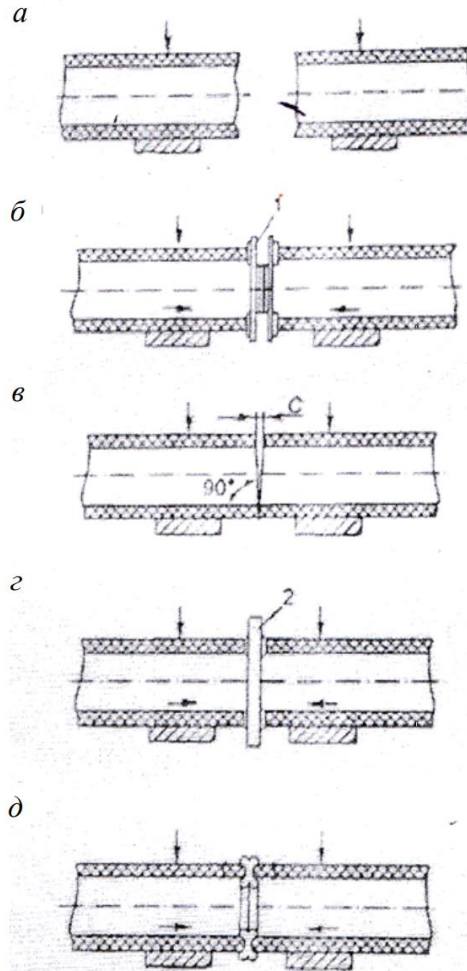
Последовательность процесса сборки и сварки встык труб из полиэтилена:
